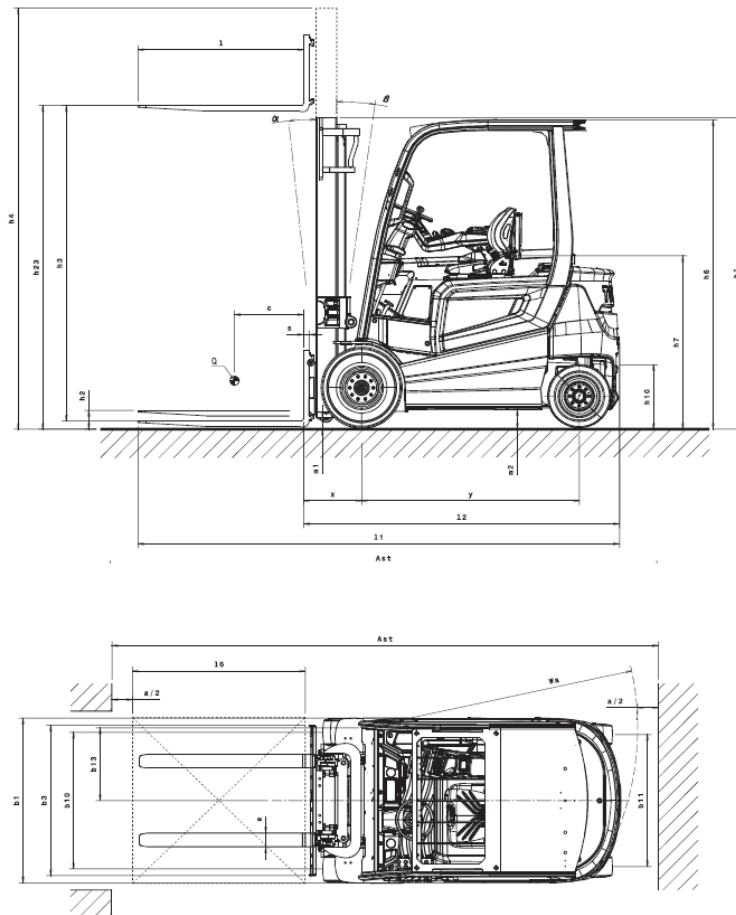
Загальний вигляд навантажувача Toyota Traigo80, 4-wheel 2.5t [15].
